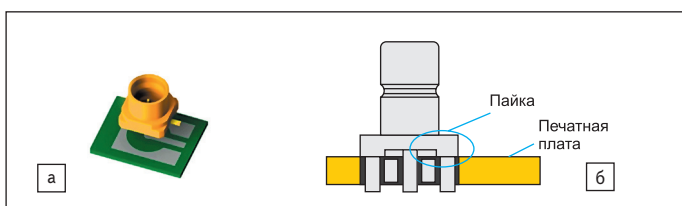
Монтаж соединителей: а) поверхностный; б) в отверстия печатной платы
